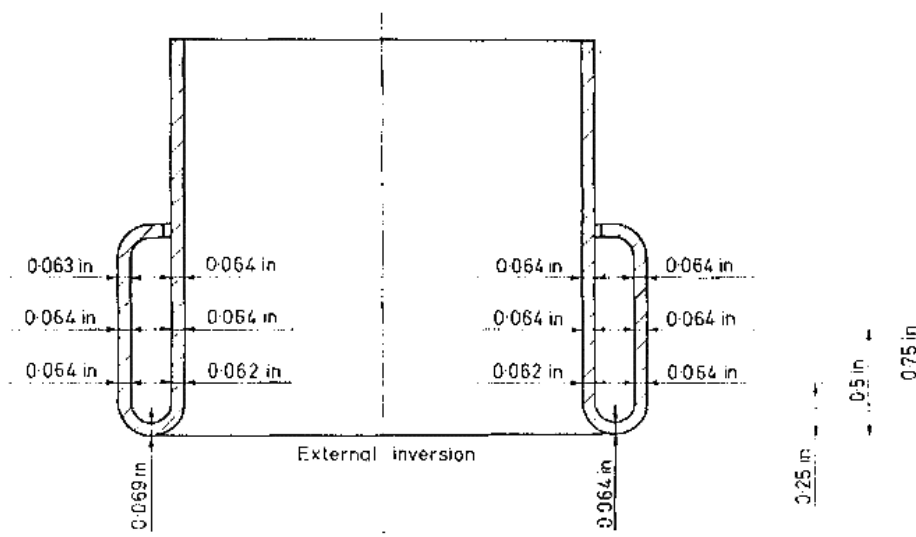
misurazione sperimentale dello spessore della parete di un elemento tubolare soggetto a 'inversion tube'. [29]
